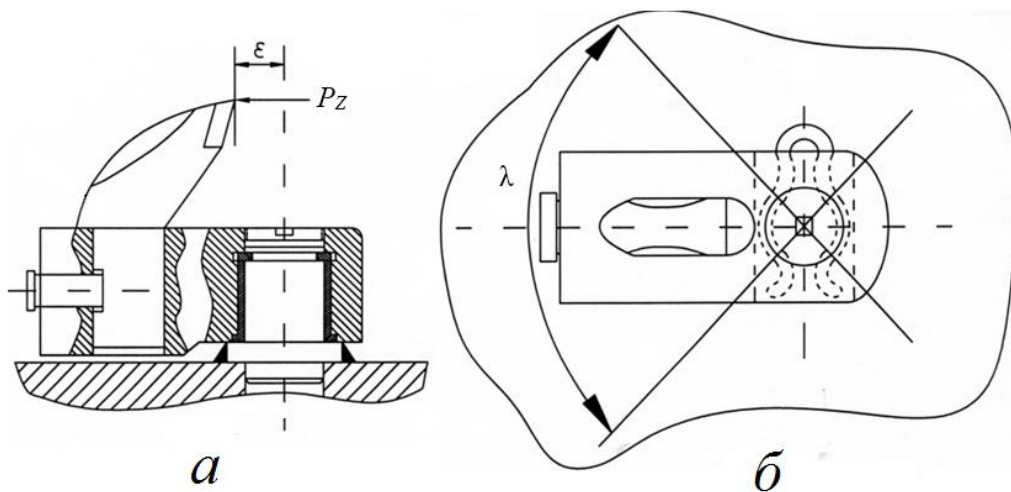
Схема устройства для крепления радиального резца на исполнительном органе горного комбайна: а – вид сбоку; б – вид сверху
